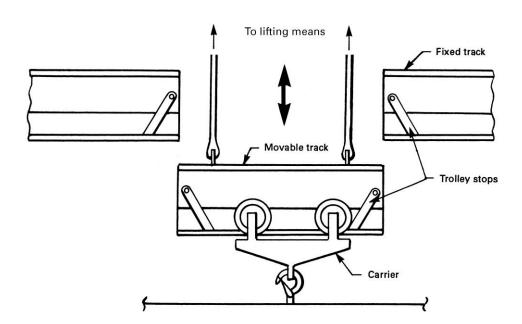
Sistema de enclavamiento para grúa suspendida
